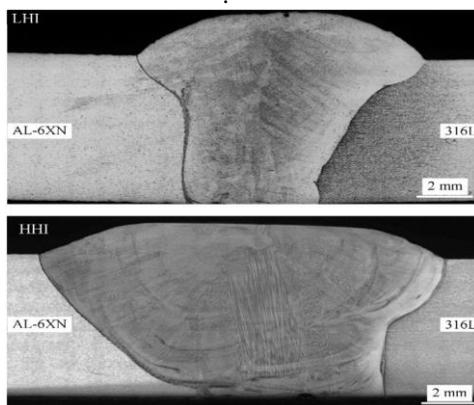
Micrografías de la soldadura disímil AL6XN y 316L
